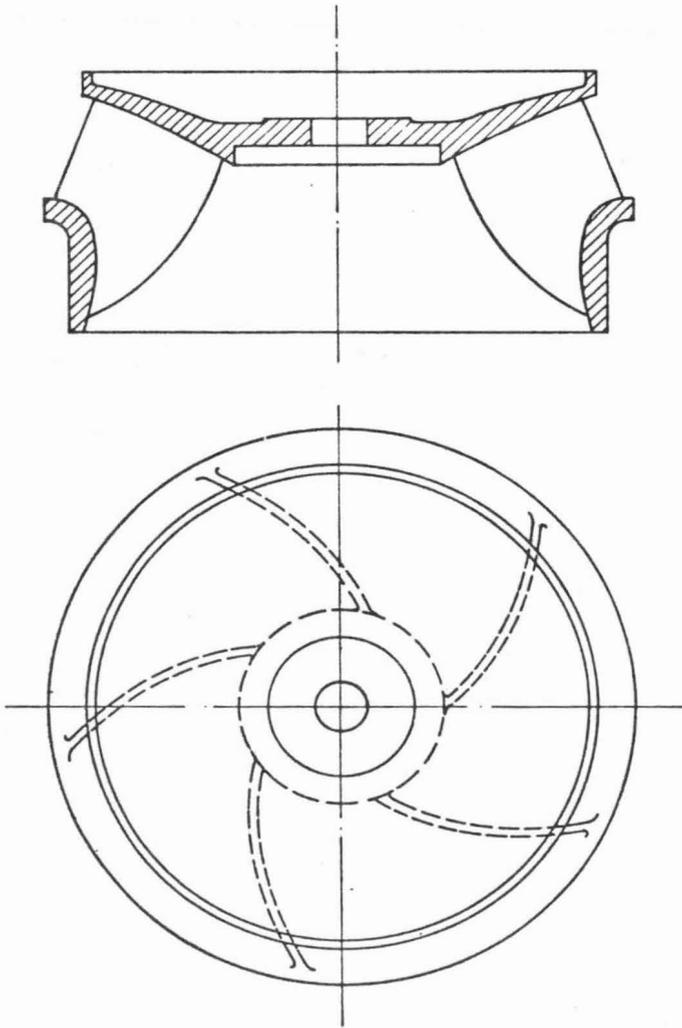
ROTOR FRANCIS MONOBLOCO
